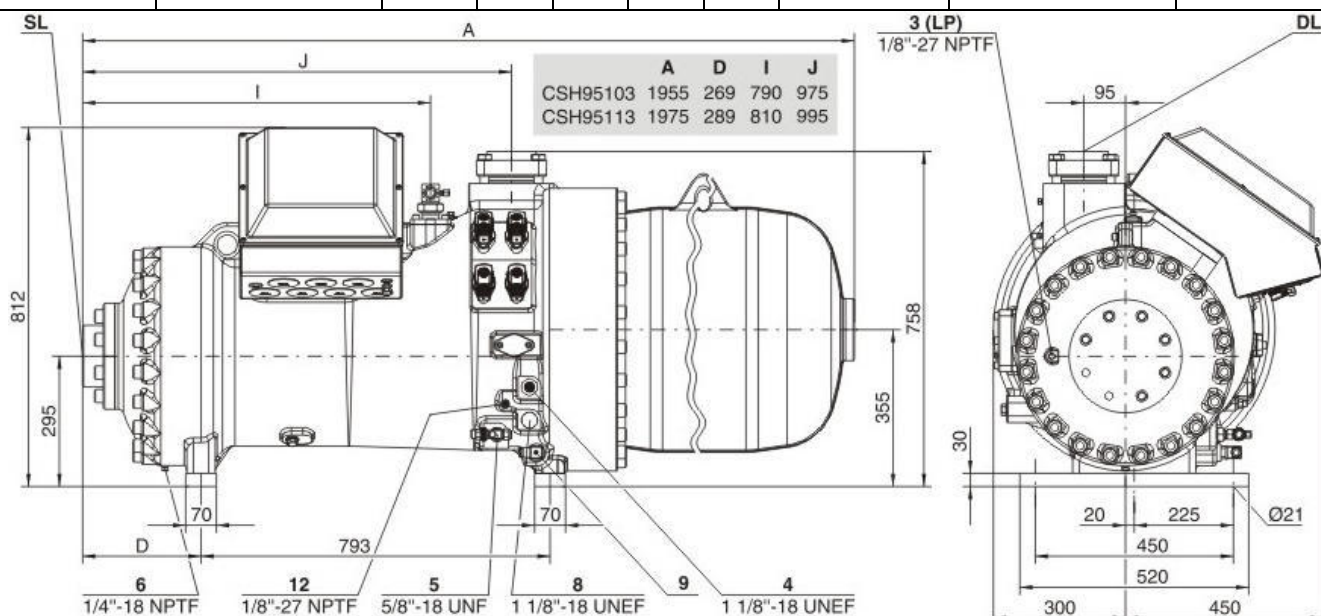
Загальний вигляд компресора Bitzer CSH95113-320Y
